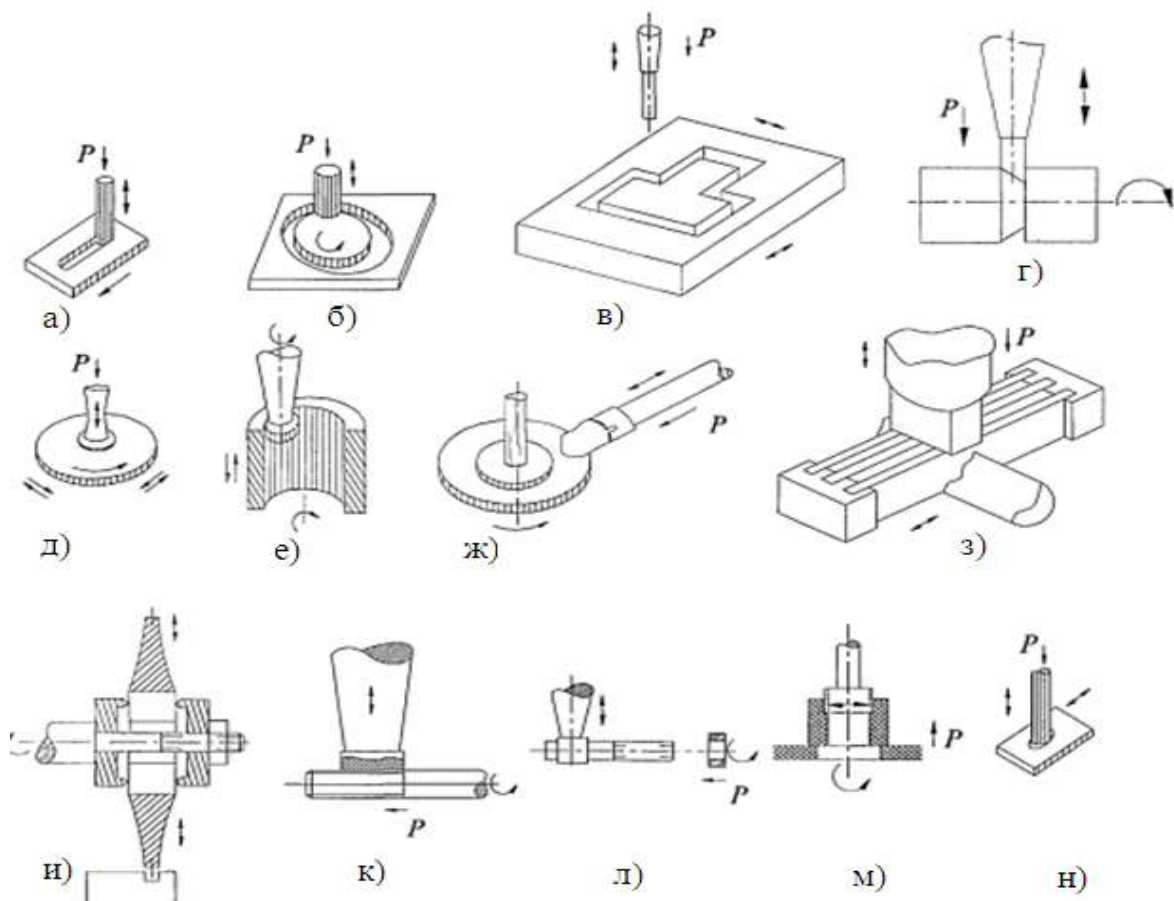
Основні схеми виконання технологічних операцій ультразвукової механічної обробки заготовок: а – прорізання канавок; б – вирізання дисків; в – обробка заготовок складного фігурного контуру; г – точіння; д – плоске шліфування торцом круга; е – внутрішнє планетарне шліфування; ж – прорізання пазу і різання обертовим дисковим інструментом; з – різання багатолезовим стрічковим інструментом; и – різання дисковим випромінювачем; к – нарізання зовнішньої різьби гребінцем; л, м – нарізання внутрішньої різьби; н – обробка еліптичного отвору
